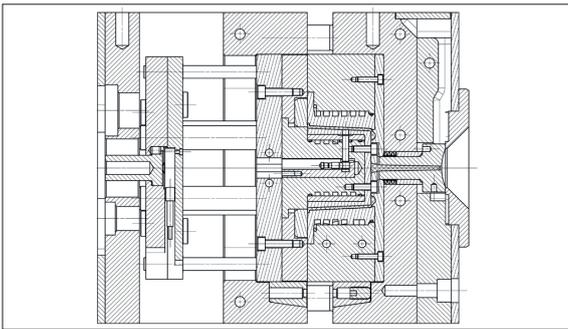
Querschnitt durch das Becherwerkzeug mit integrierter Kraftmessung im Auswerferpaket und im Werkzeugkern
